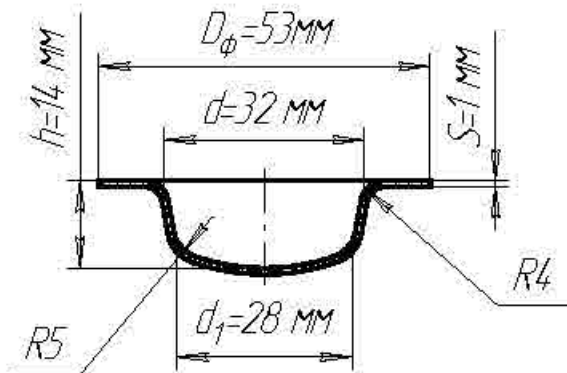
Ескіз до розрахунку геометричних параметрів заготовки
